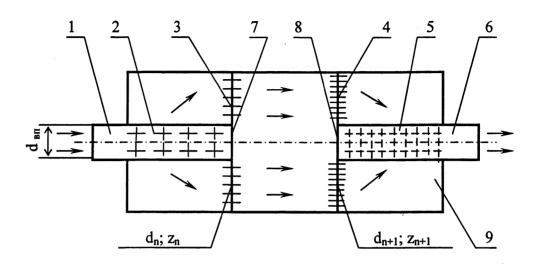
Принципиально-коструктивная схема глушителя. 1 — впускной патрубок; 2 — входная центральная труба; 3 — входная поперечная перегородка; 5 — выходная центральная труба; 6 — выпускной патрубок; 7,8 — заглушка; 9 — корпус глушителя;  $d_{B\Pi}$  — диаметр впускного патрубка;  $d_{\Pi}$  — диаметр отверстий перфорации n-го внутреннего элемента;  $z_{\Pi}$  — количество отверстий перфорации в n-ом элементе.
